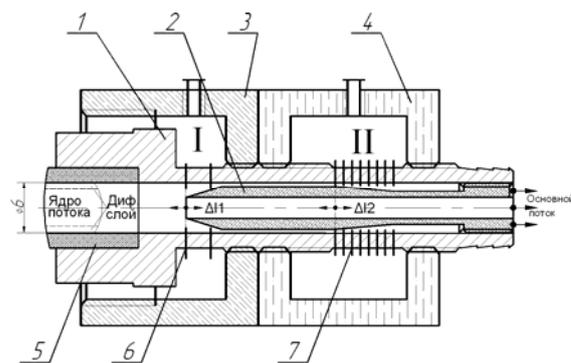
Устройство для отвода диффузионного слоя: 1 – корпус; 2 – полый шток; 3 – первый кожух; 4 – второй кожух; 5 – керамическая мембрана; 6 – кольцевые отверстия корпуса первой области отвода; 7 – кольцевые отверстия корпуса второй области отвода; I – первая область отвода; II – вторая область отвода
